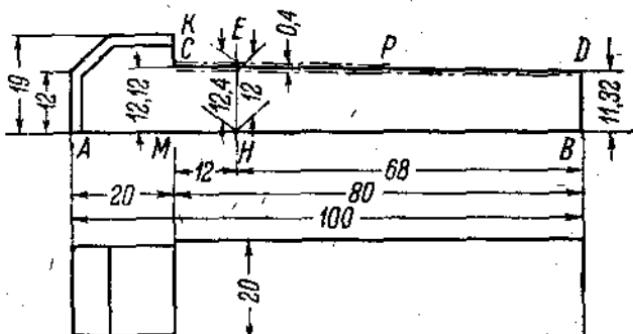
Обработка клиновой врезкой шпонки с головкой.
